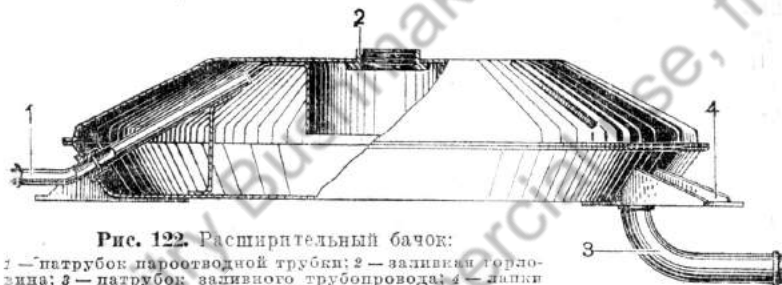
Расширительный бачок: 1 — патрубок паропроводной трубки; 2 — заливная горловина; 3 — патрубок заливного трубопровода; 4 — лапки крепления
